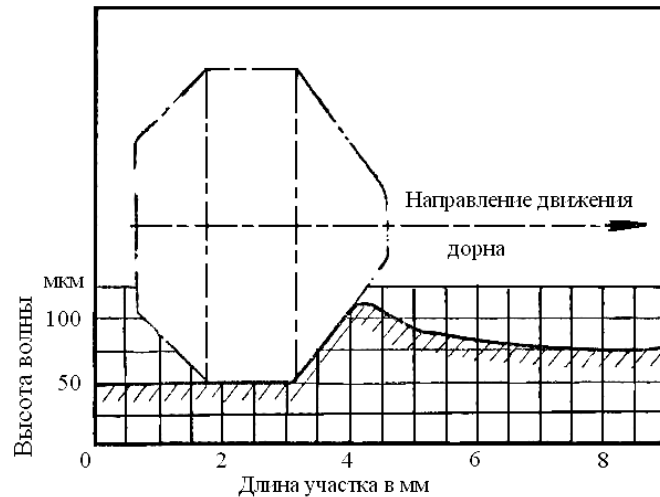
Профиль пластической волны металла, получающейся при дорновании в отверстии [5]
